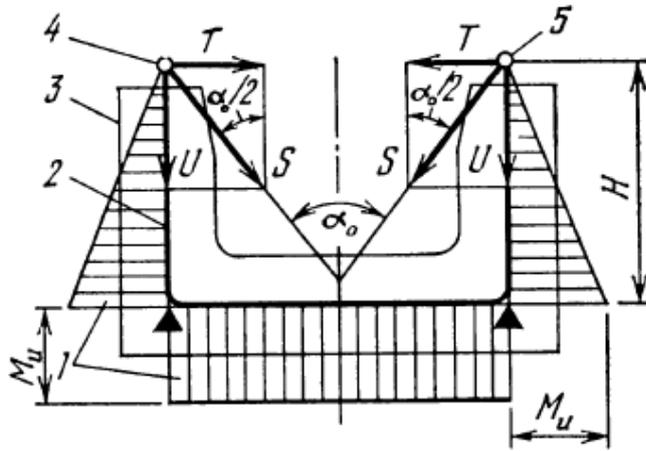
Схема нагружения опорной стойки цепного кантователя.
